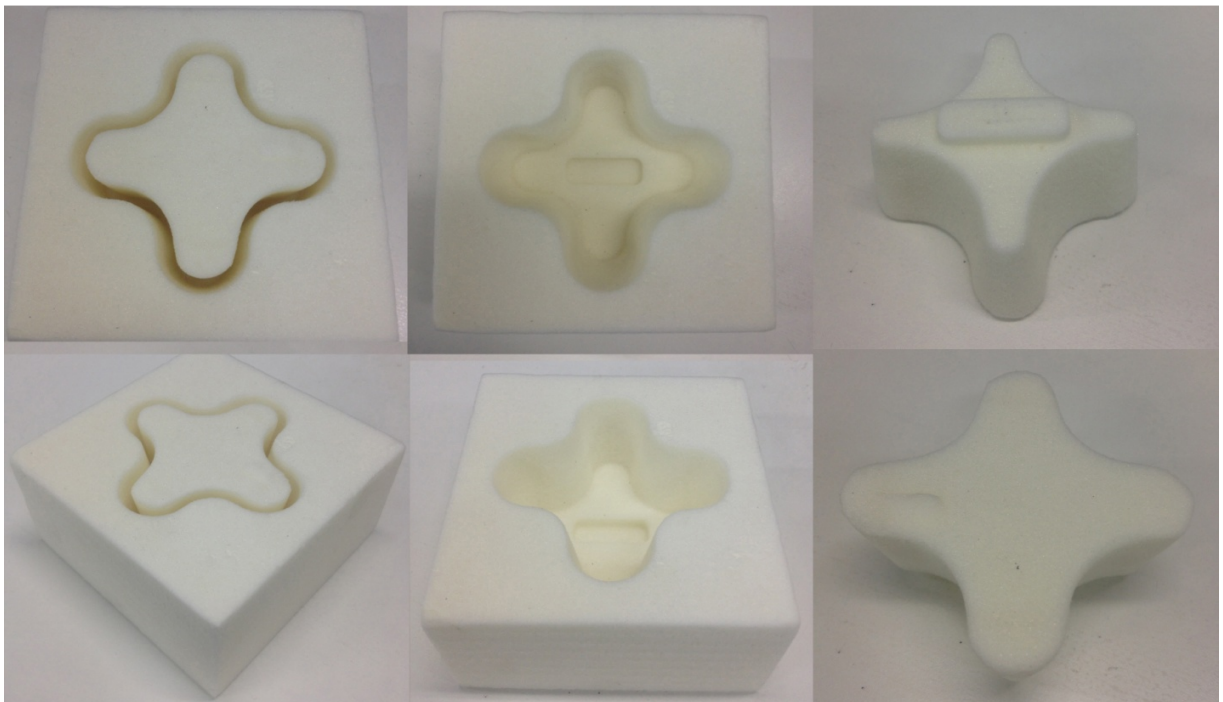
Exemplo de geometria complexa bipartida para possibilitar a usinagem em máquina CNC de três eixos.
